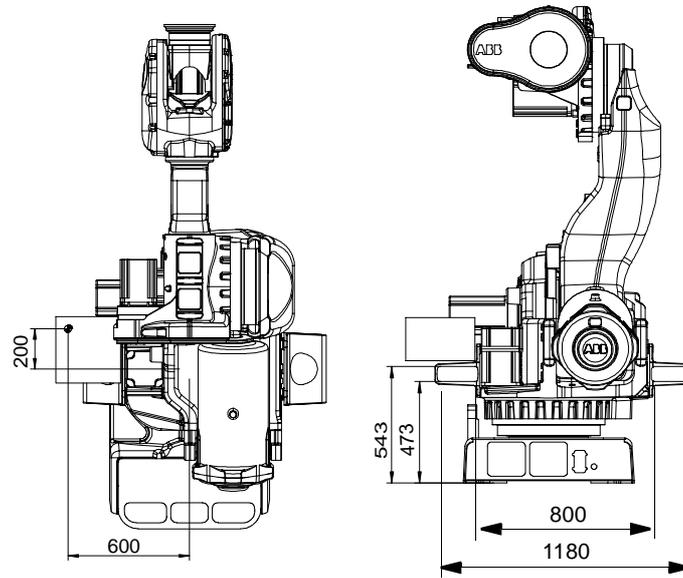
Charge supplémentaire sur le châssis du robot IRB 7600 (dimensions en mm).
